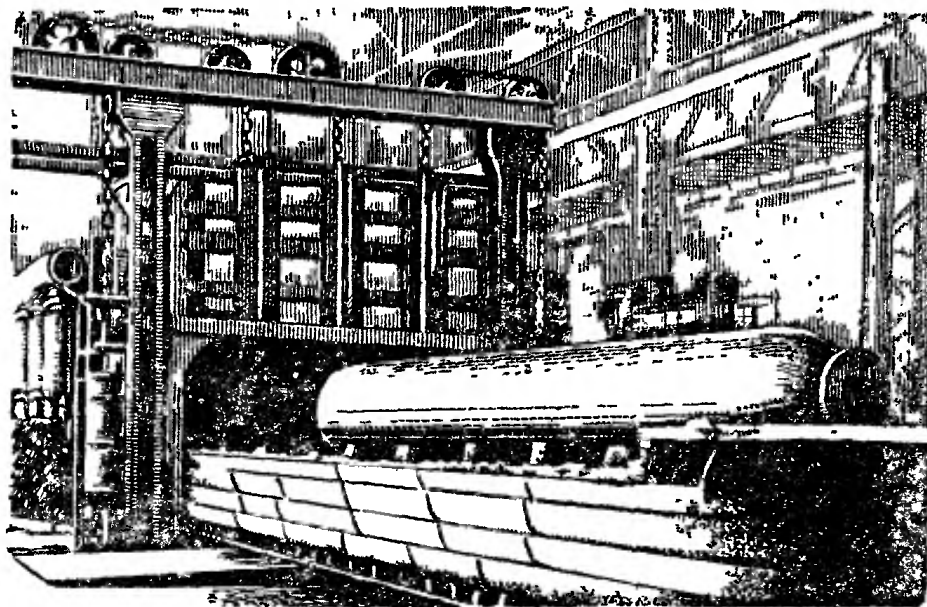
Печь с выдвижным подом для отжига и нормализации сварных барабанов котлов высокого давления
